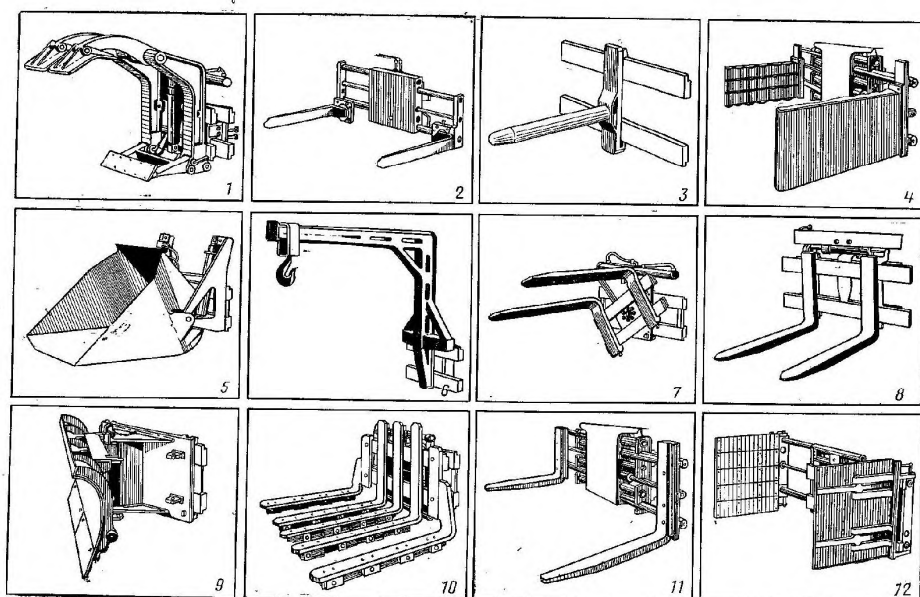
Сменные рабочие приспособления для малогабаритных погрузчиков:
